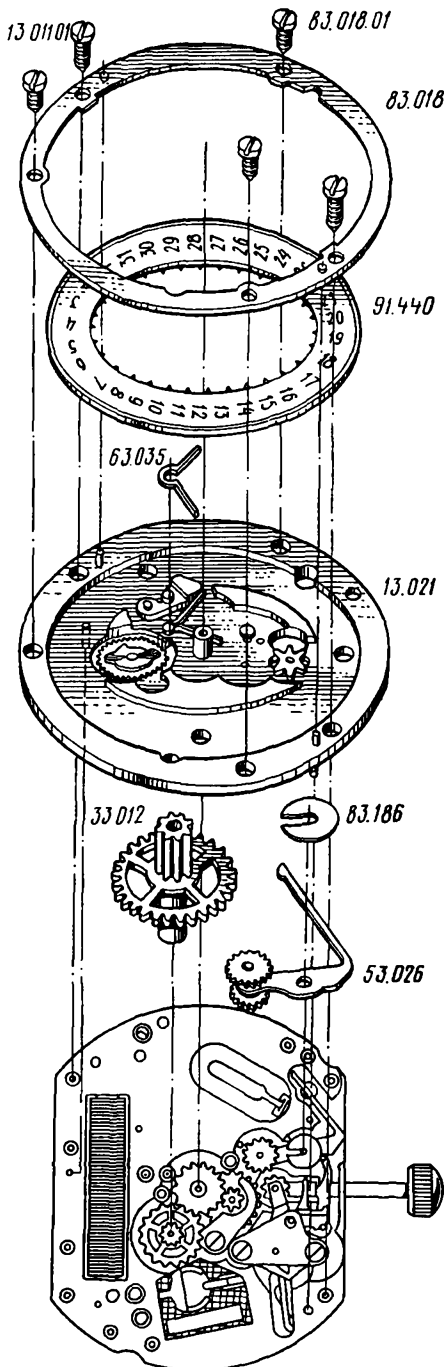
Детали и сборочные единицы календарного устройства механизма часов 2460:
